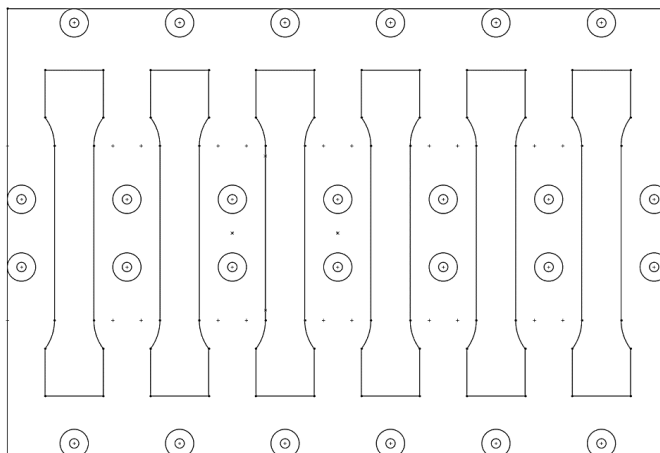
Esboço em *Solidworks* da chapa a ser usinada.
